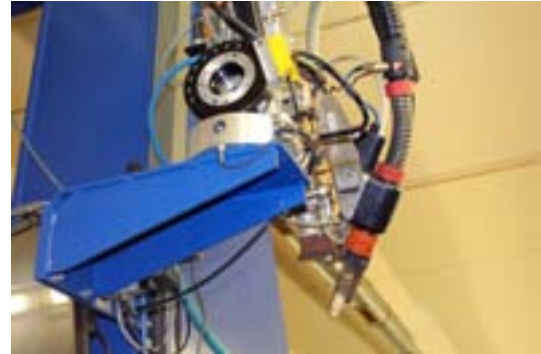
Automatisch läuft auch die Brennerreinigung an dieser Station.
